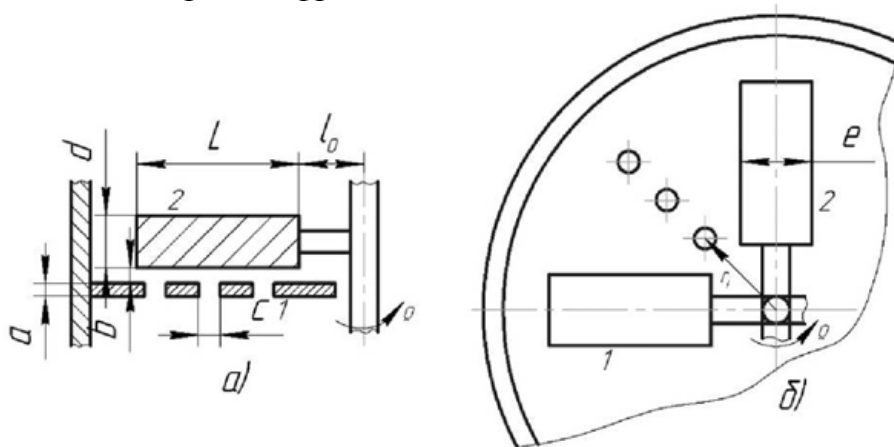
Розрахункова схема: а – вид в перерізі, б – вид зверху
